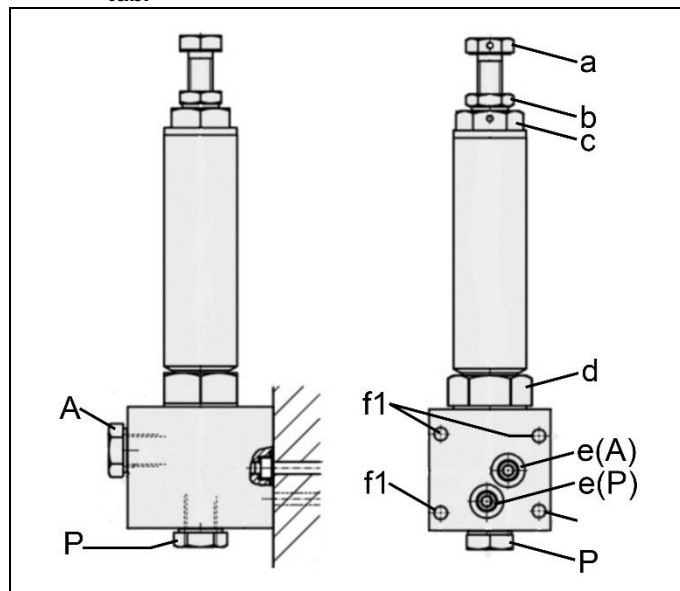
Valvola con collegamento a flangia o raccordi per tubi
